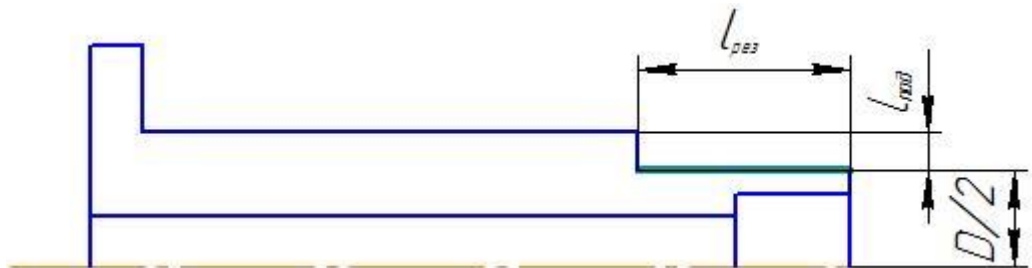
Траектория точения цилиндрической поверхности согласно РТК
